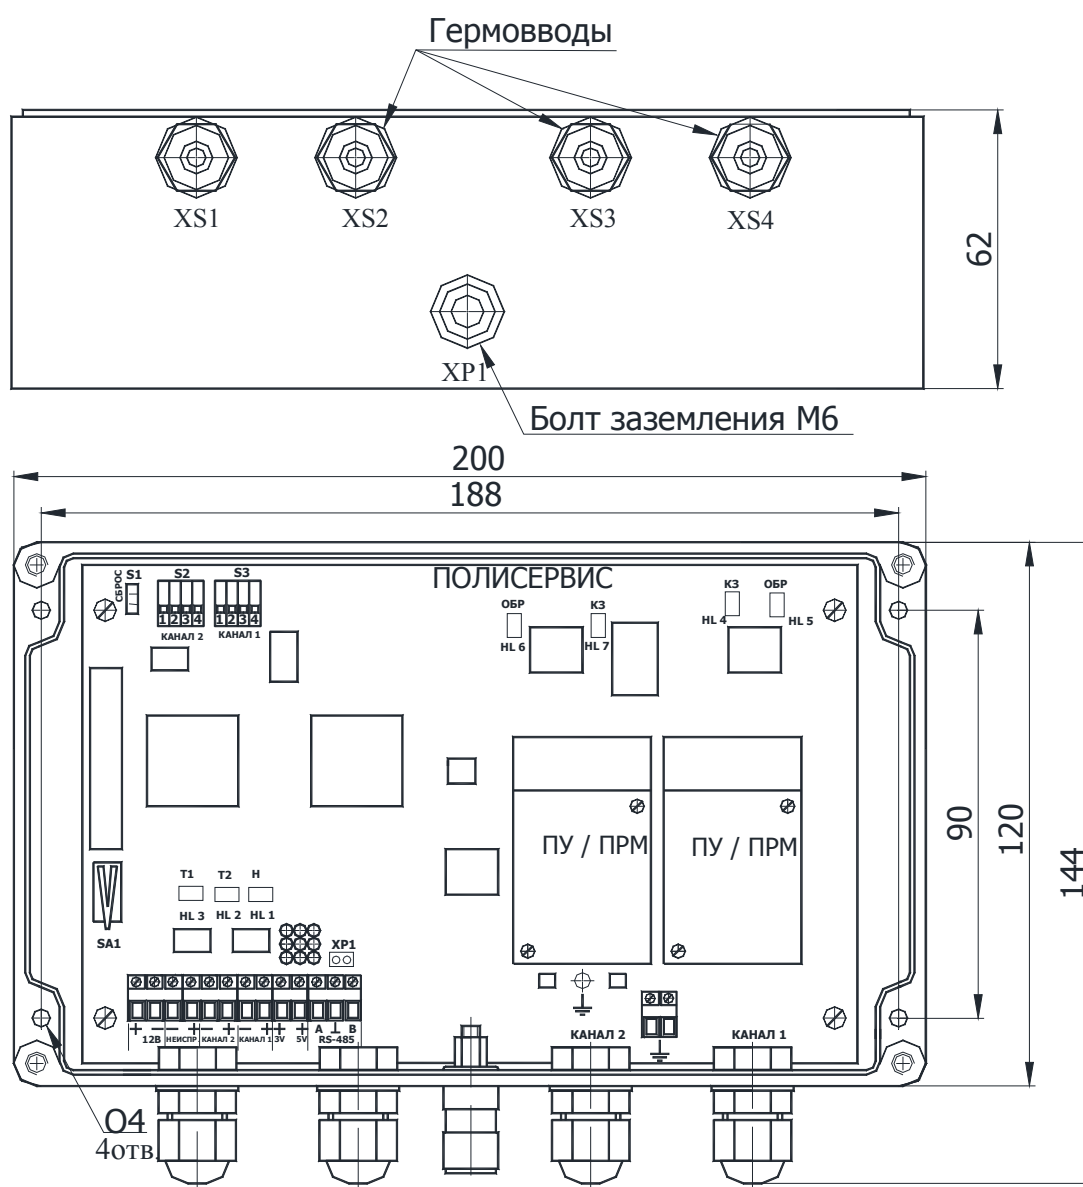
Общий вид БОС (поликарбонатный корпус).
